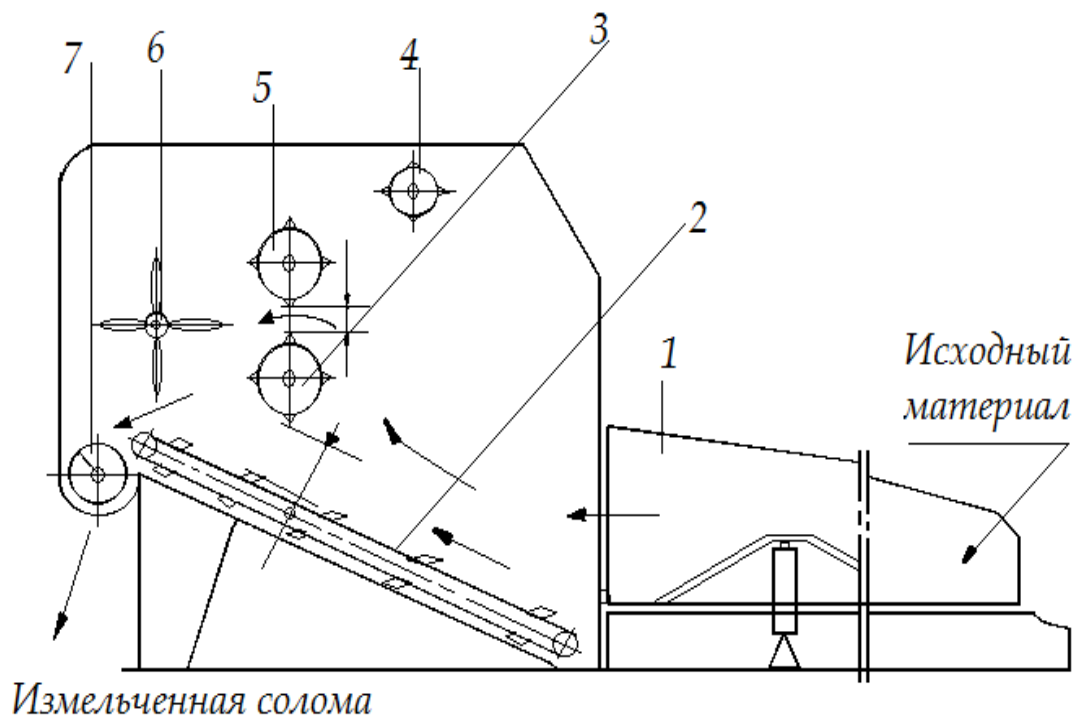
Схема и общий вид питателя-измельчителя:
